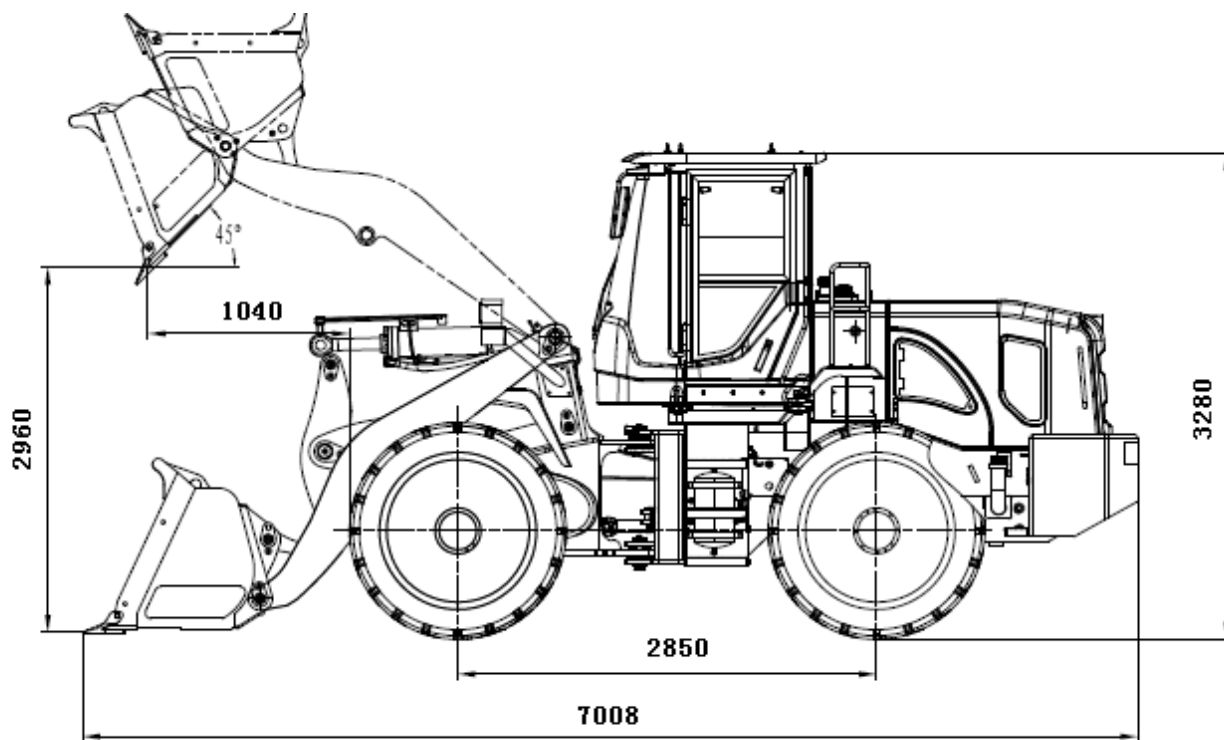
Схема габаритного размера погрузчика стандартной подъемной стрелы с Deutz AG WP6G125E23
